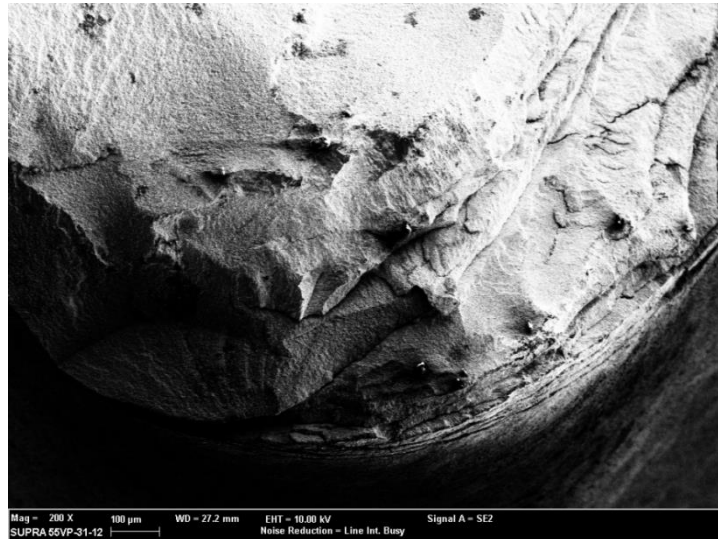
Detalhe da região fraturada da ferramenta de corte utilizada nos ensaios pilotos.
